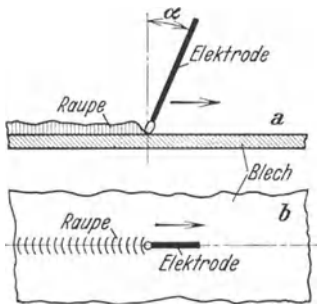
Elektrodenhaltung in Schweißrichtung.
